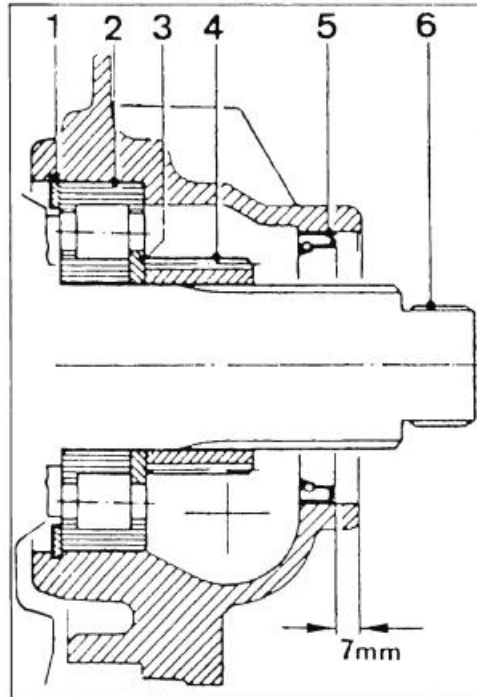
Частковий розріз задньої частини коробки перемикання передач:
